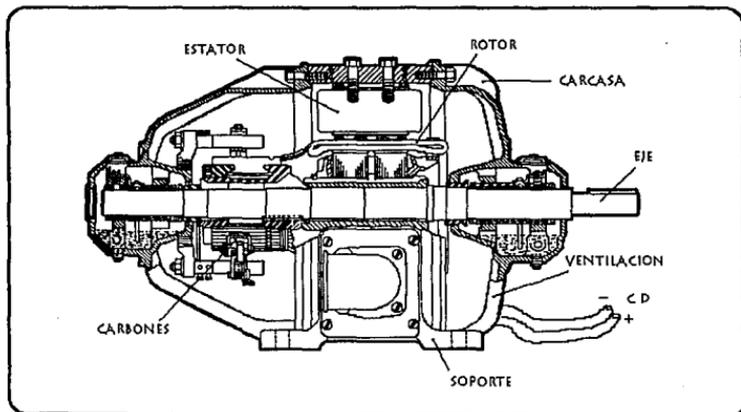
CORTE REPRESENTATIVO DE UN MOTOR DE CD.
